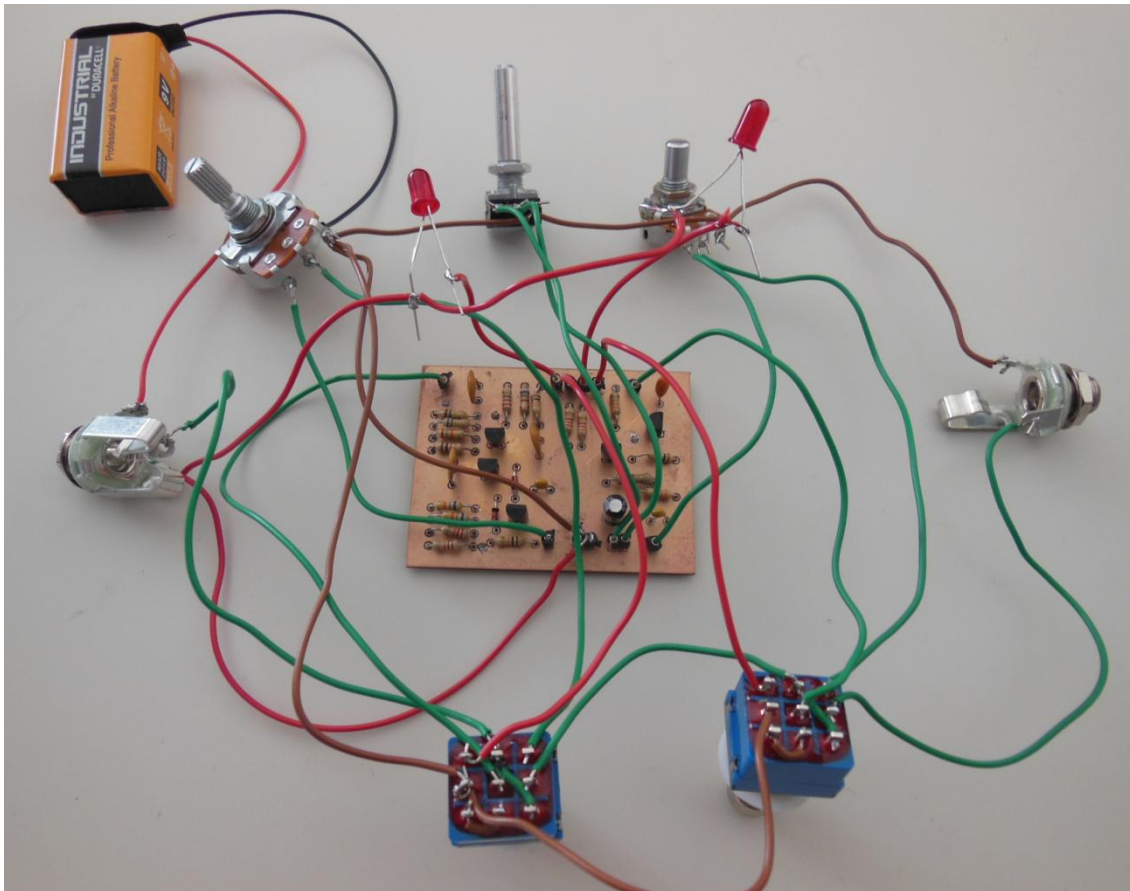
PCB CON TODOS LOS COMPONENTES CONECTADOS
